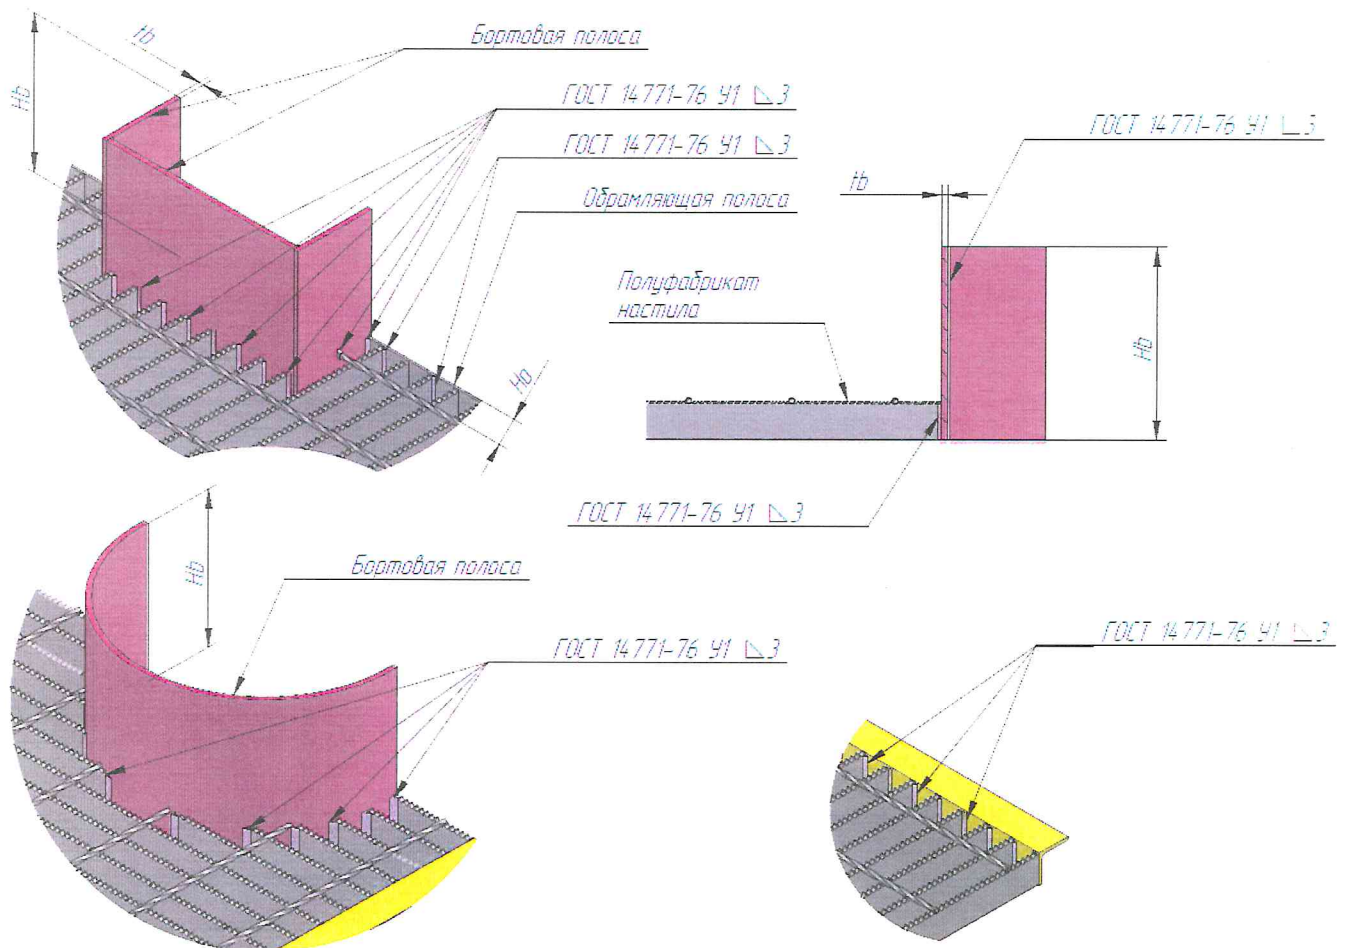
Пример выполнения сварки обрамляющего уголка и бортовой полосы.
